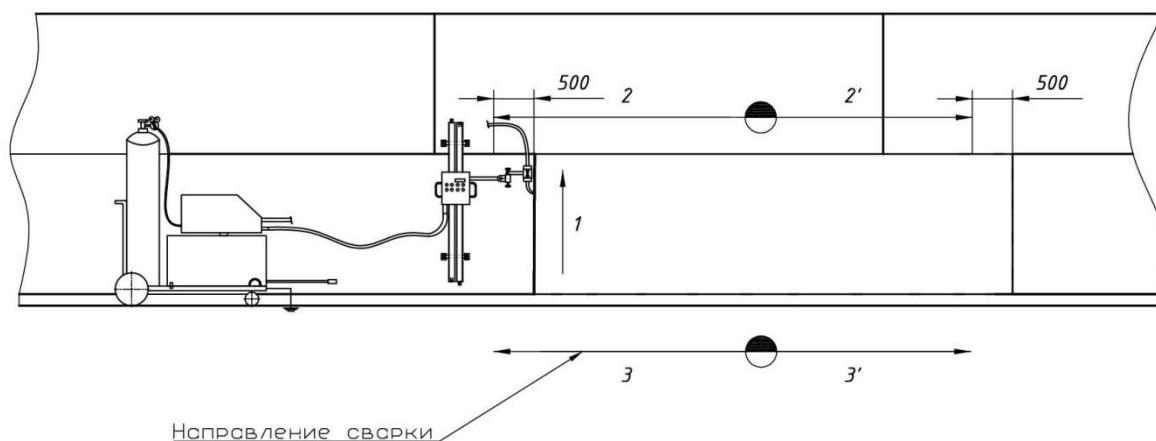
Эскизная схема разработанной технологии монтажной сварки
